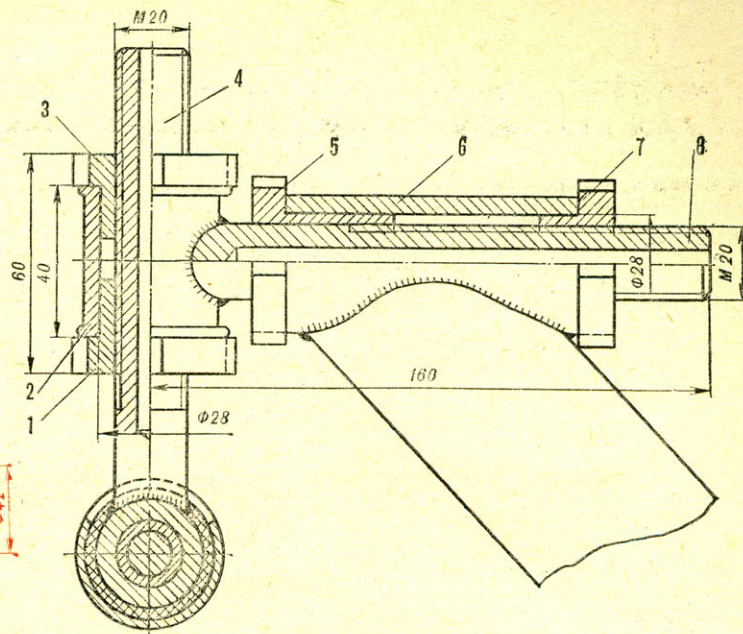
Механизм регулировки клиренса и развала передних колес:
